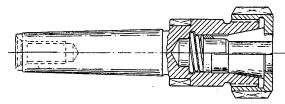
Bohr- und Fräsfutter mit Morsekegel (Eugen Fahrion, Esslingen-Mettingen)
